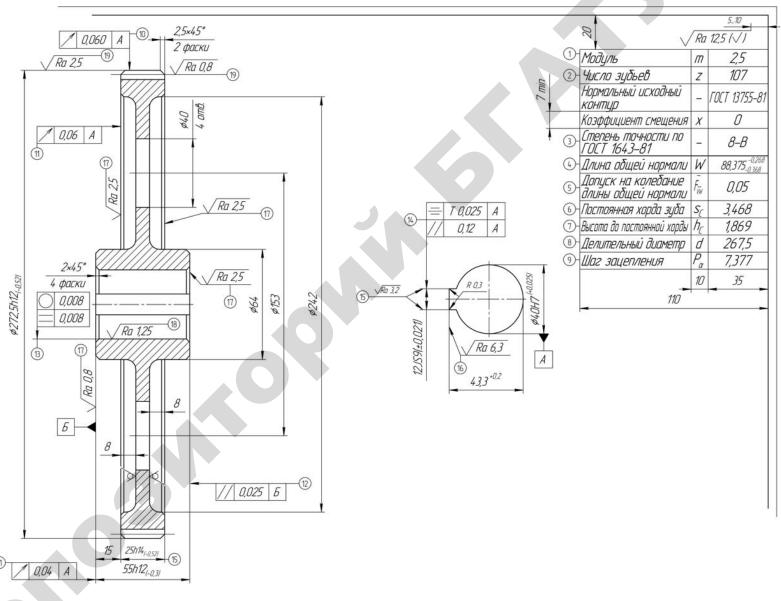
Схема простановки размеров и показателей точности для цилиндрического зубчатого колеса
